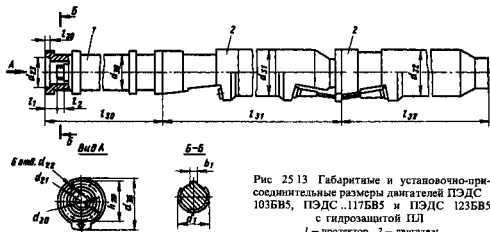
13 Габаритные и установочно-при- соединительные размеры двигателей ПЭДС 103БВ5, ПЭДС 117БВ5 и ПЭДС 123БВ5 с гидрозащитой ПЛ 1 — протектор, 2 — двигатель
